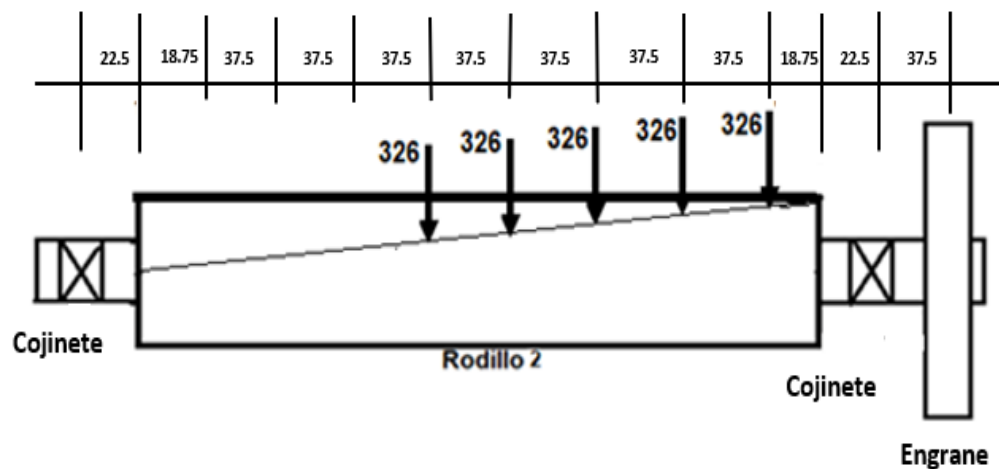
14. Geometría del eje del rodillo 2. Los componentes que están conectados al rodillo 2 son engrane, cojinetes y pasadores.
